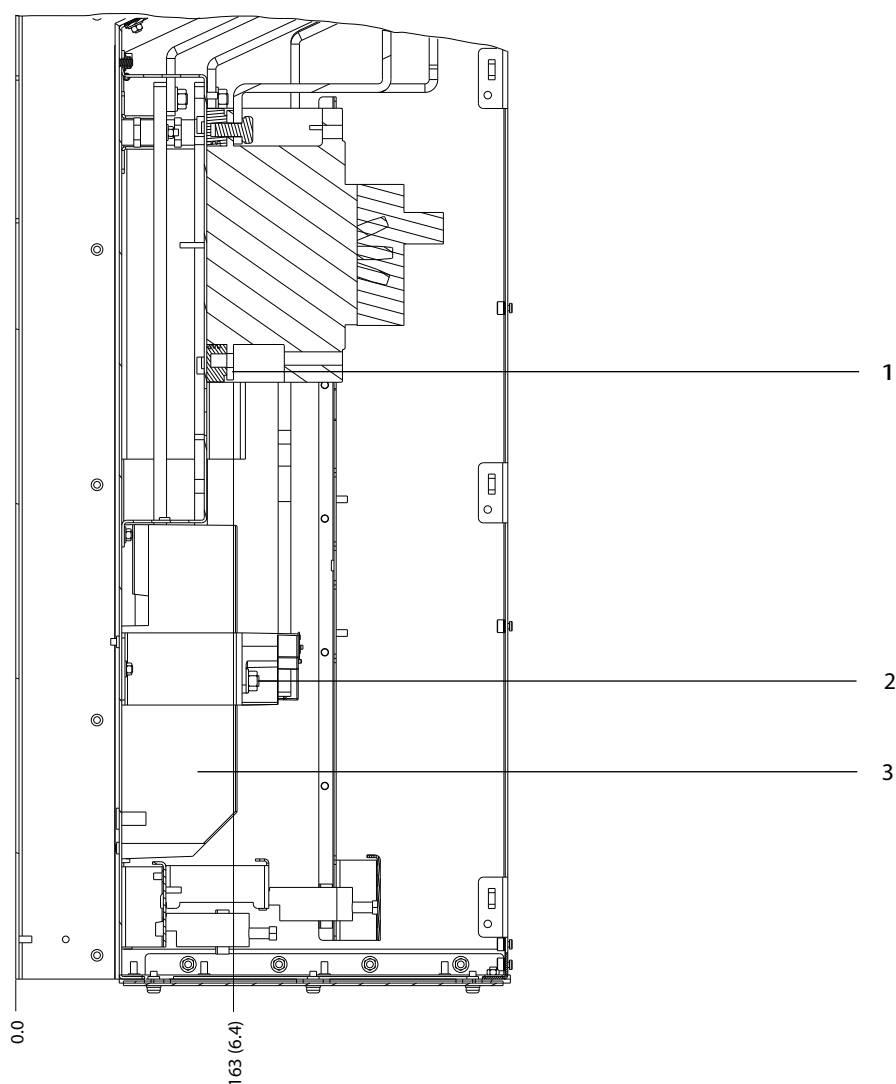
Dimensions des bornes D6h avec options contacteur et sectionneur (vues latérales)
